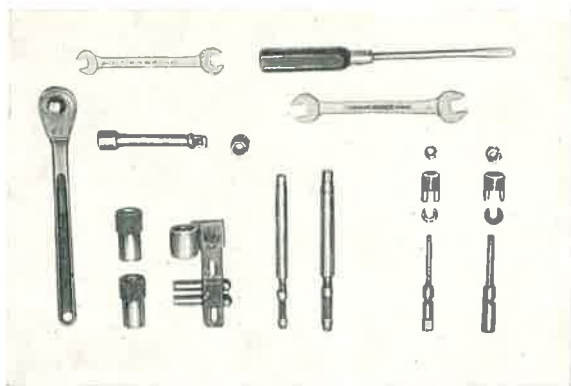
Zusammenstellung der Werkzeuge, wie sie für die Arbeit Gruppe M Motor M 20 gebraucht werden.
